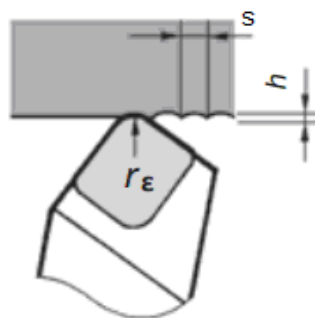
Схема образования шероховатости поверхности при точении [4]
